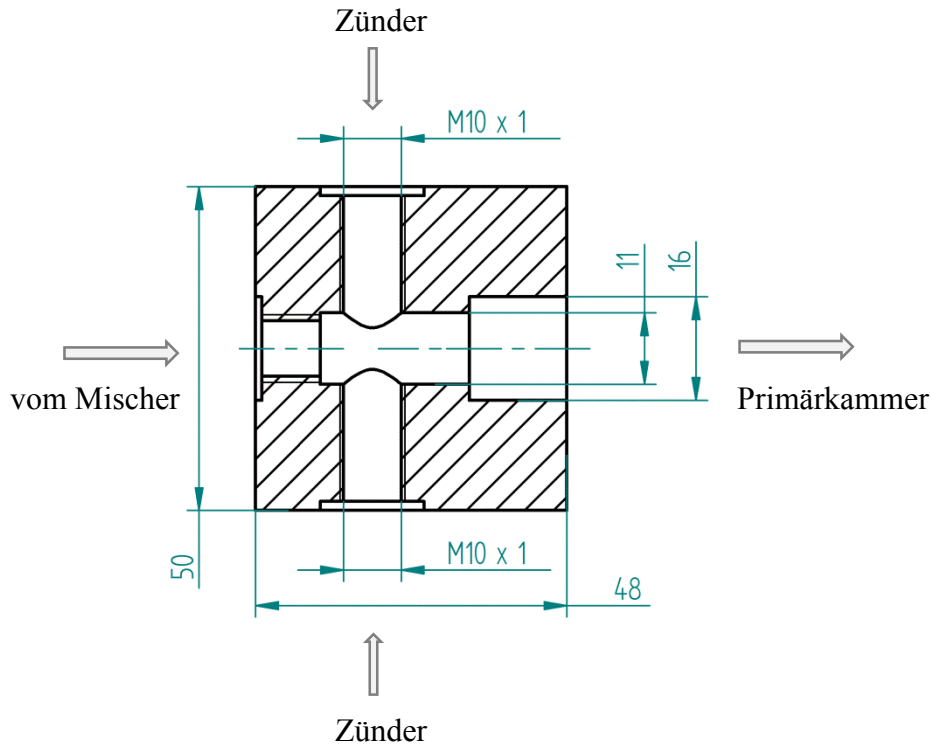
Querschnitt des Zündblocks. Alle Abmessungen in Millimeter.
